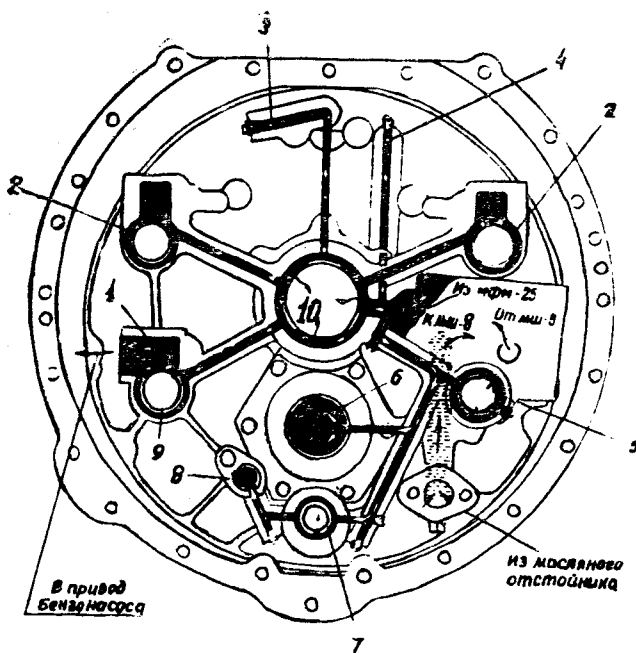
Схема масляных каналов в задней крышке картера (вид со стороны двигателя): 1—подшипник привода БНК-12БК и счетчика оборотов; 2—подшипник привода магнето; 3—подвод масла к масляному манометру; 4—канал подвода масла к приводу РПО; 5—подшипник привода МШ-8М; 6—ось двойной шестерни привода крыльчатки нагнетателя; 7—подшипник привода генератора; 8—ось промежуточной шестерни привода генератора; 9—подшипник двойной шестерни привода генератора, магнето, БНК-12БК и АК-50М; 10—подшипник валика привода агрегатов
